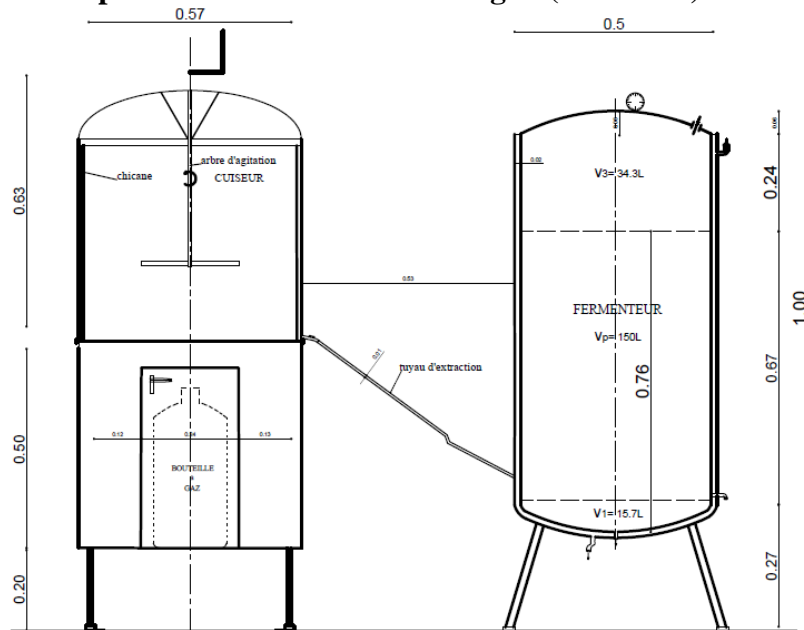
Dessin du biofermenteur en coupe (B-B) et plan
